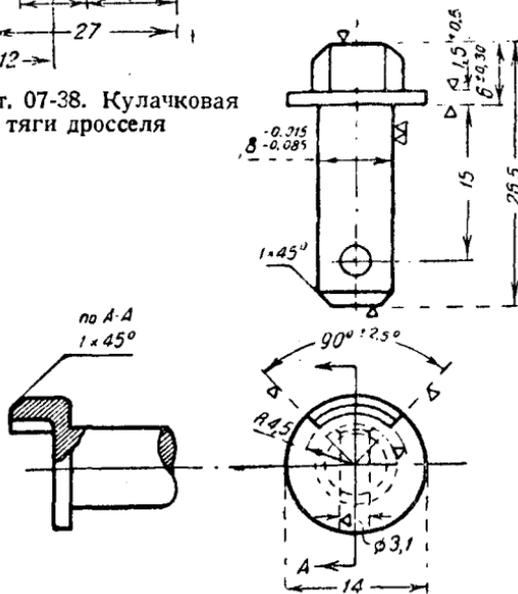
Дет. 07-43. Кулачок крышки дросселя
